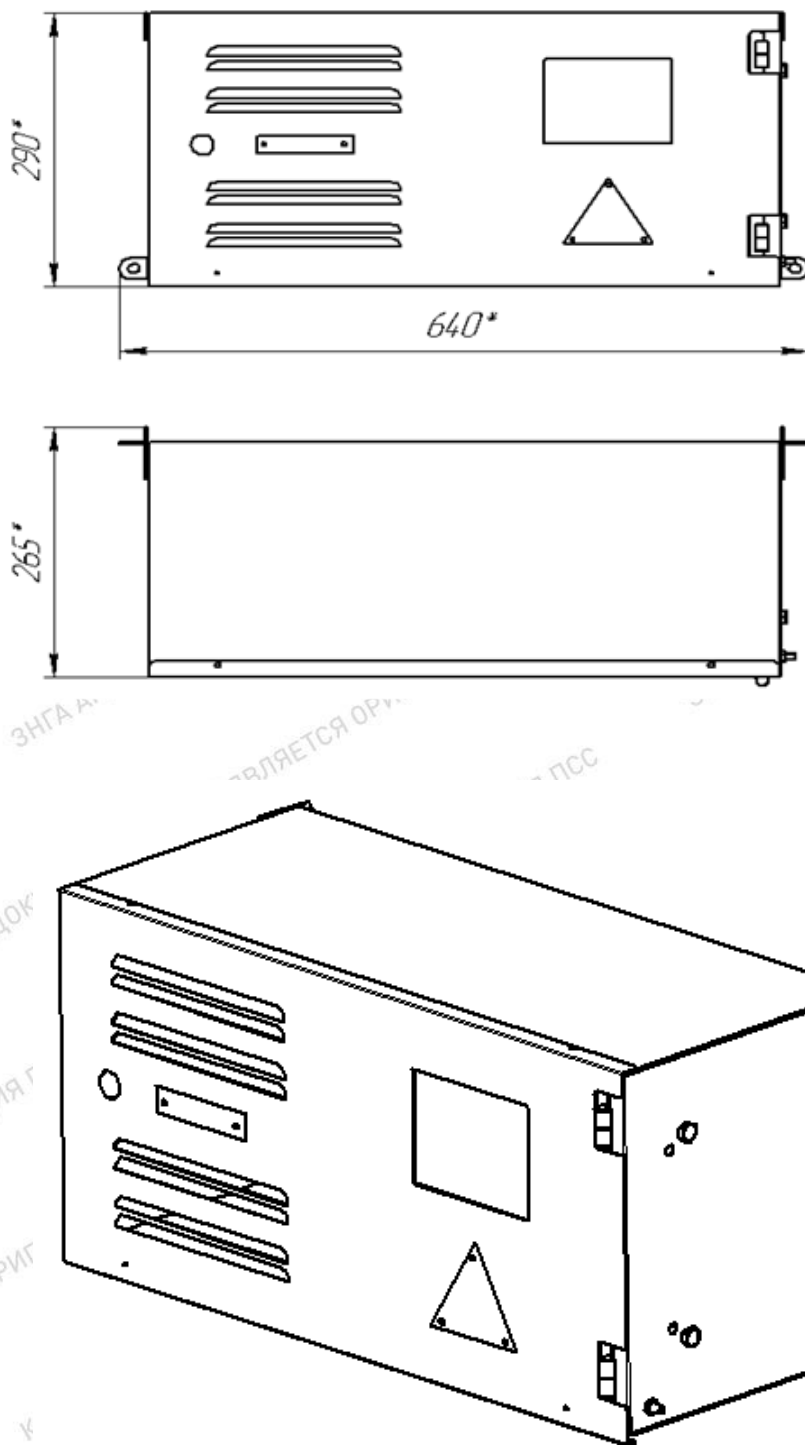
Общий вид и габаритные размеры БАР в исполнении У2
